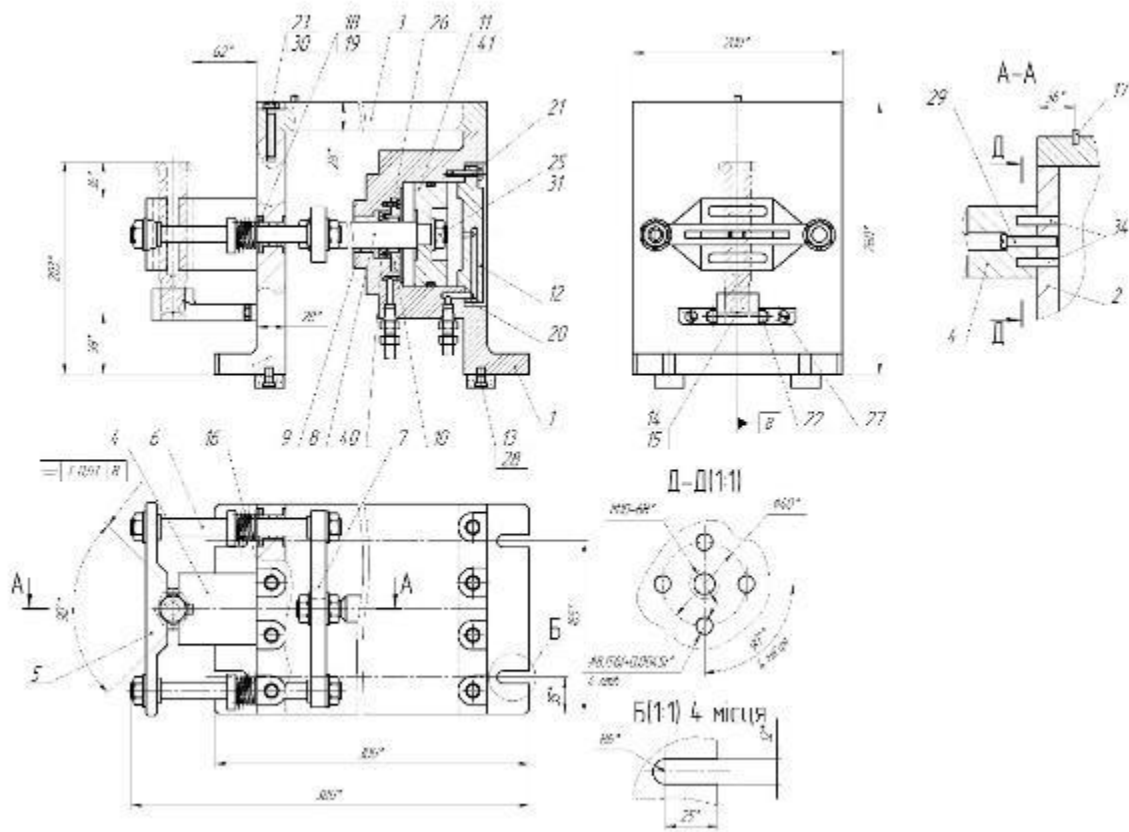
Пристосування фрезерне для обробки шестикутника
